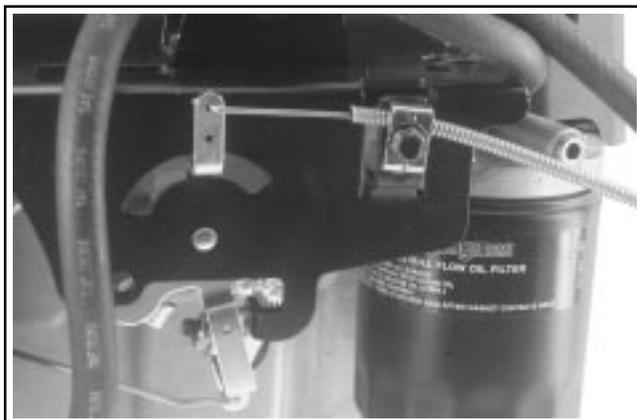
Plaque de commande de la vitesse avec commande unique de starter/accélérateur.
